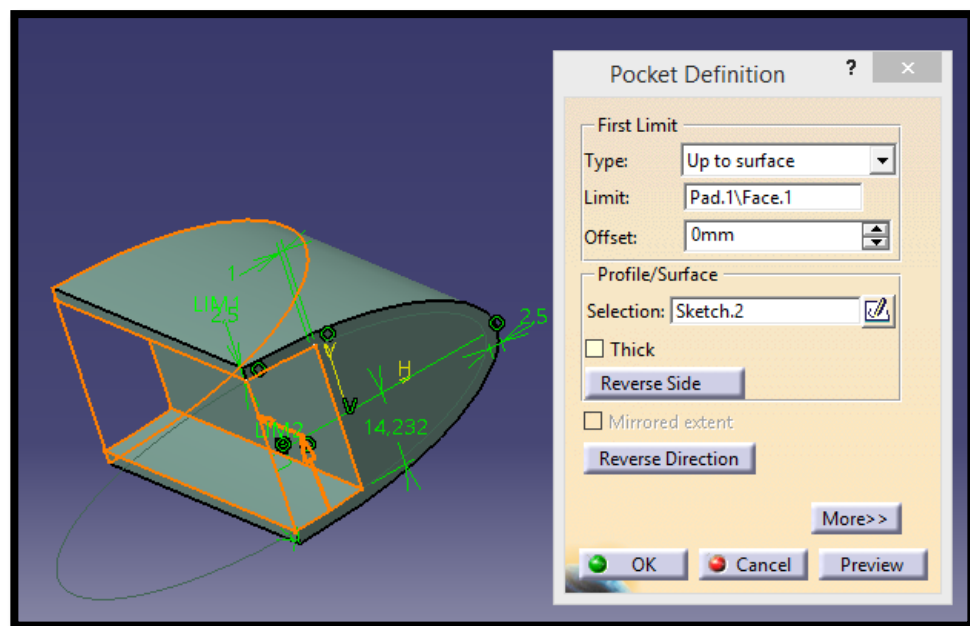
Seat mounting frame 11: Pocket pestillo 1
